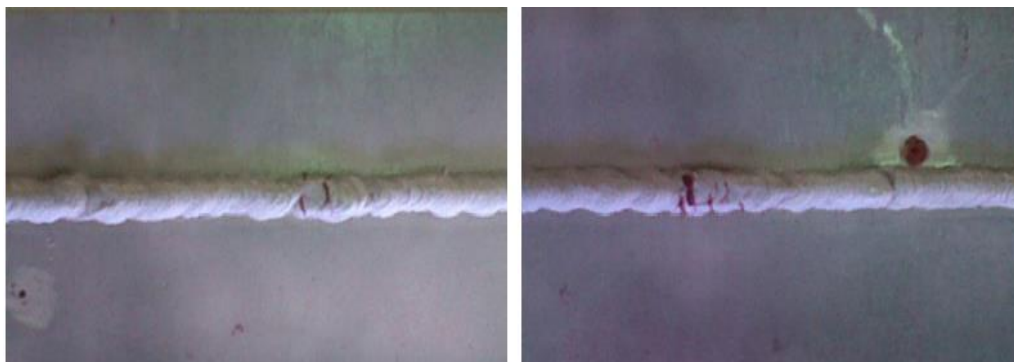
Resultados de ensaios por líquidos penetrantes de juntas soldadas
